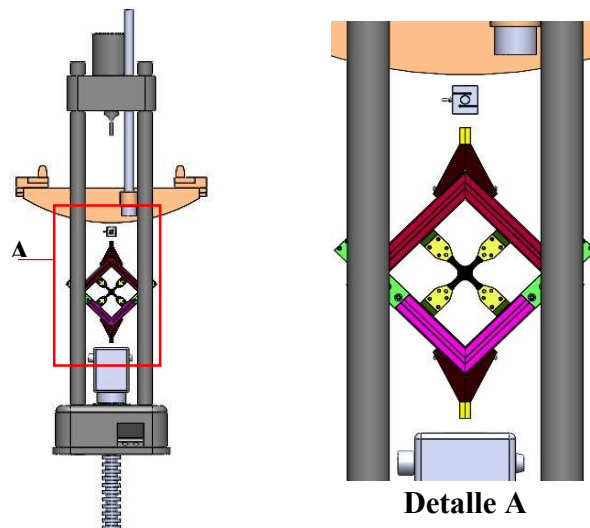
Esquema de máquina universal y dispositivo biaxial de esfuerzos
